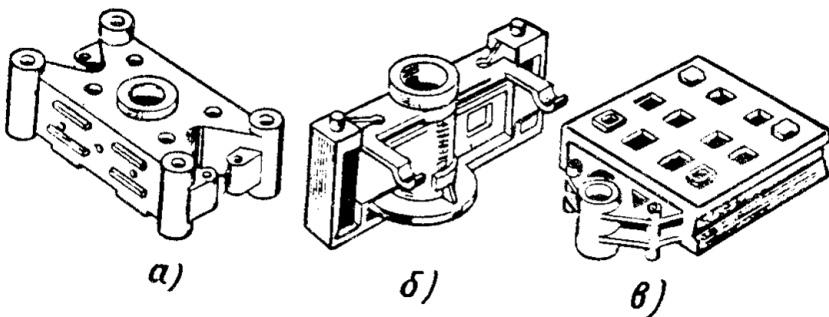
Виливки 5-ї групи (складні):
